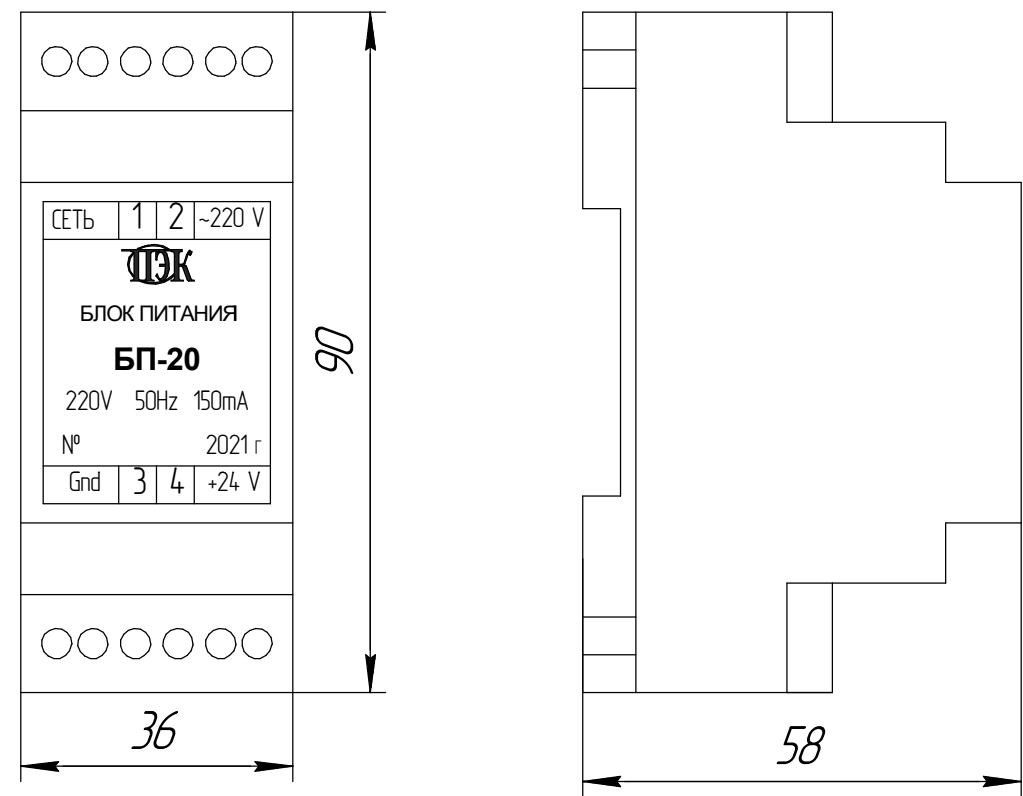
Габаритные размеры блока БП-20 на DIN-рейке
